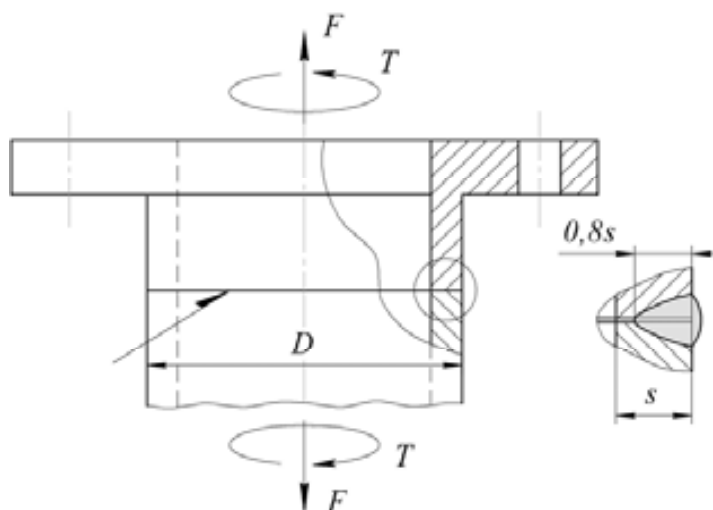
Сварное соединение встык трубы и фланца
